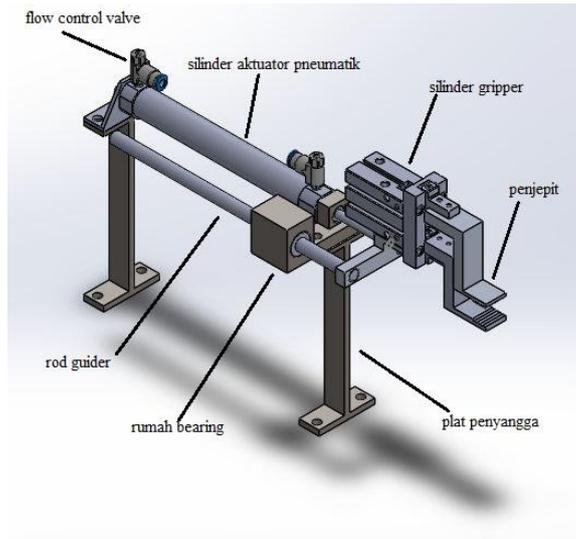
Assembly* Mesin Pengikat Sendok.
